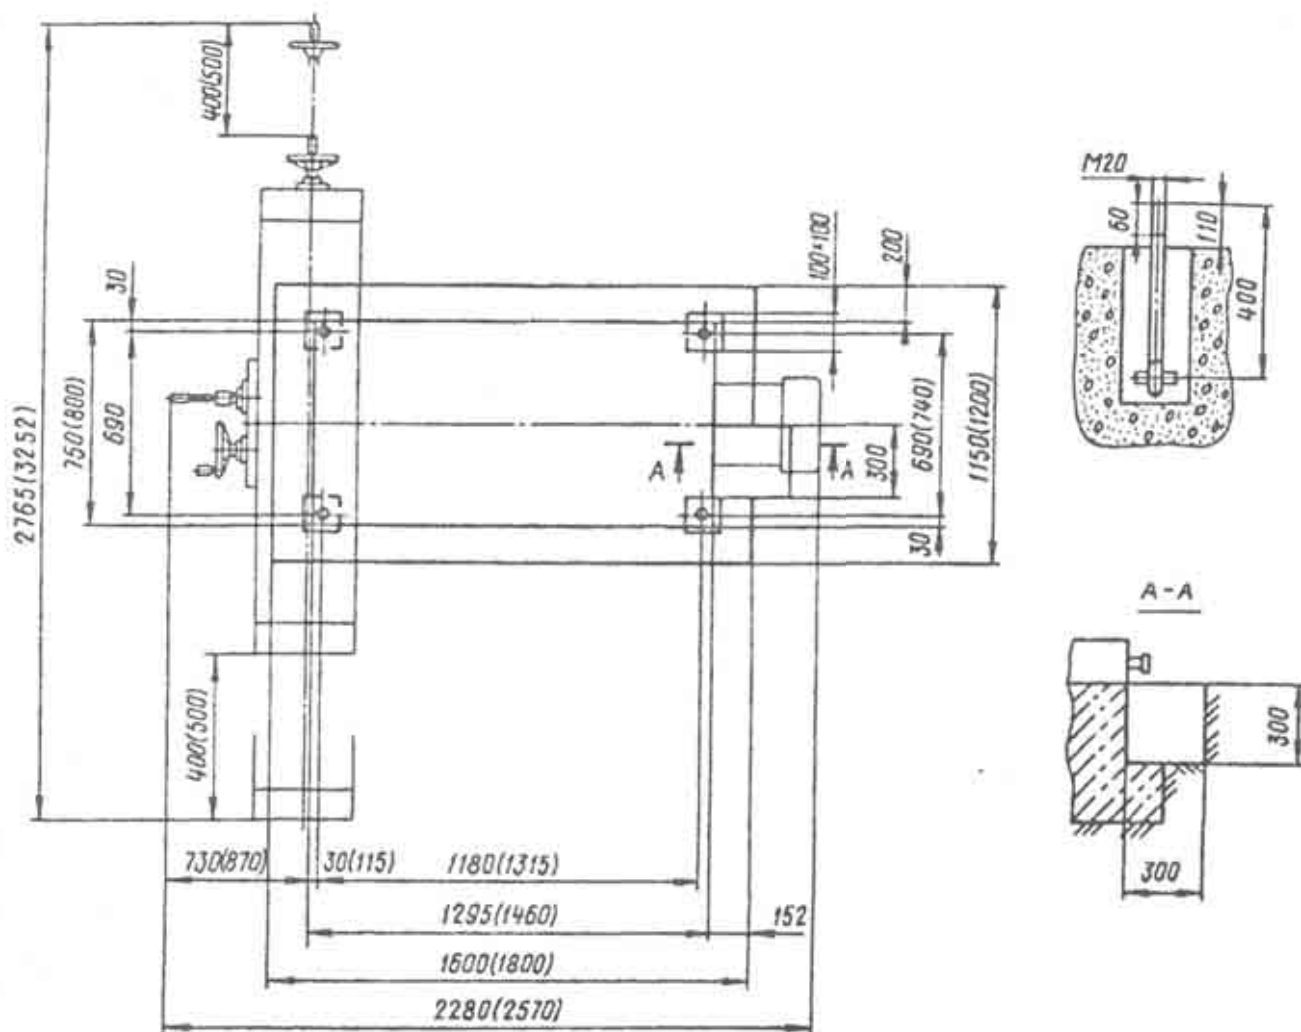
Установочный чертеж станков (в скобках размеры для станка 6Т13)
